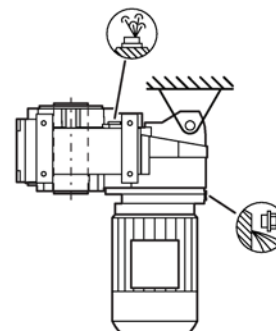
Монтажные положения для цилиндрического редуктора DF/ZF в исполнении с фланцем, типоразмеры 49 - 189 и DZ/ZZ с фланцем корпуса, типоразмеры 49-129
